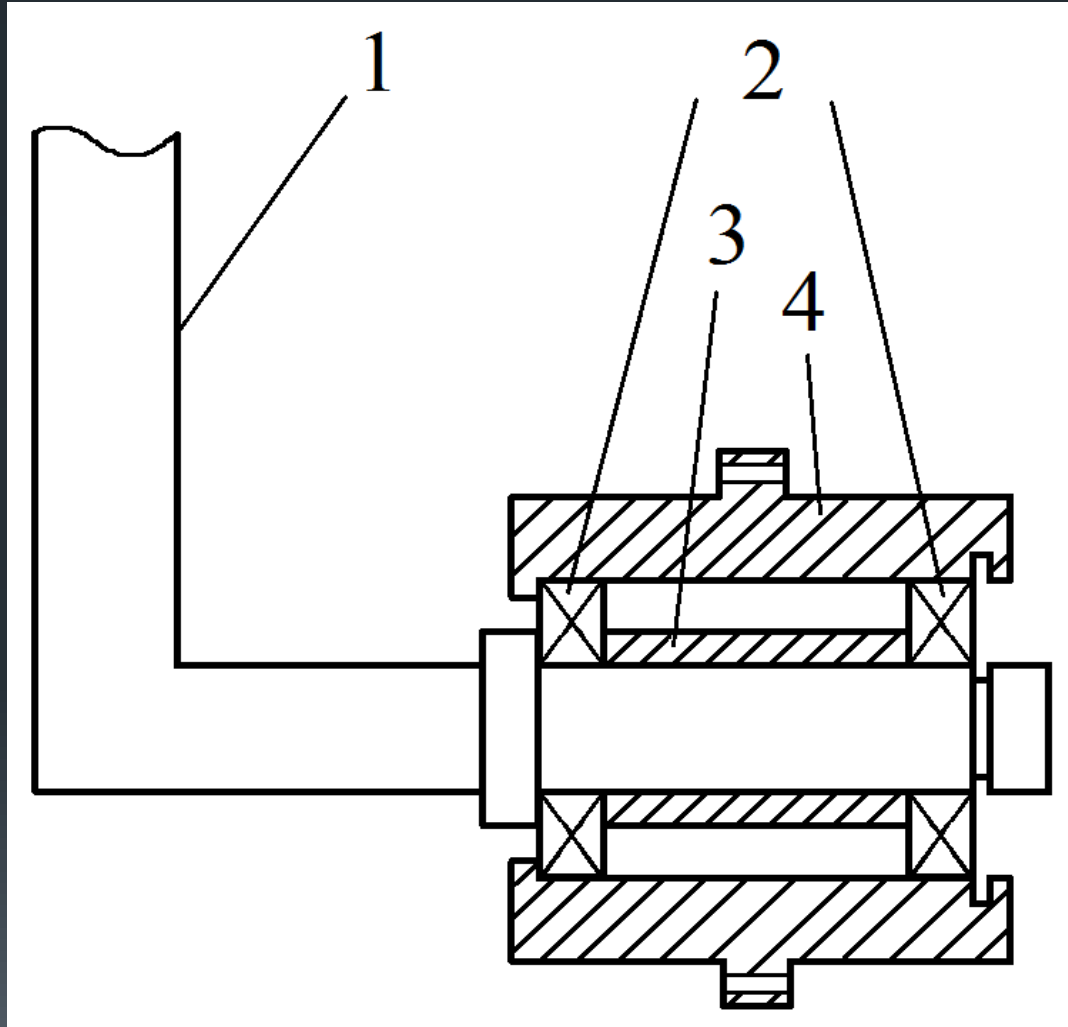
Схема узла №2; 1 – побочный вал; 2 – подшипники качения; 3 – стопорная втулка; 4 – внешняя втулка с пазами для пружин.
